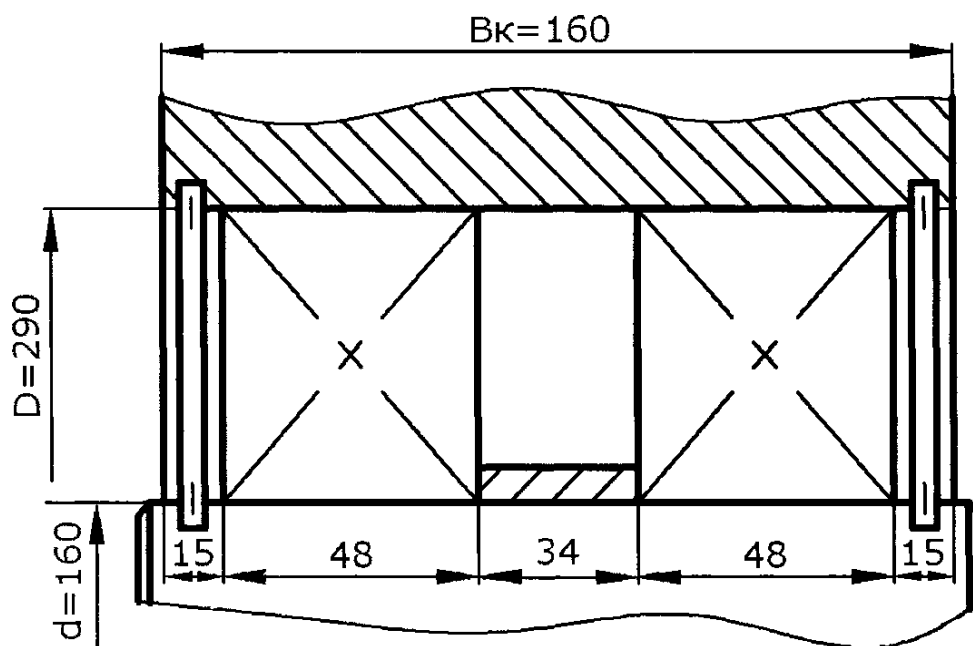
Установка роликовых подшипников № 2232 в ходовом колесе
